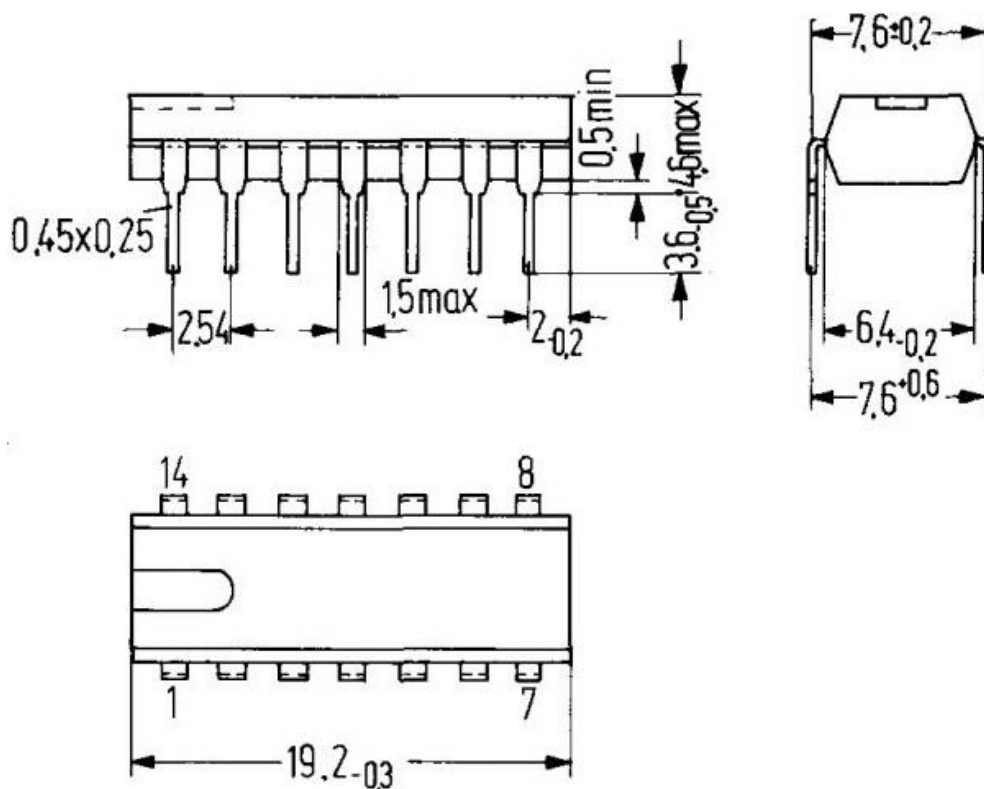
Габаритні розміри стандартного корпусу DIP-14
